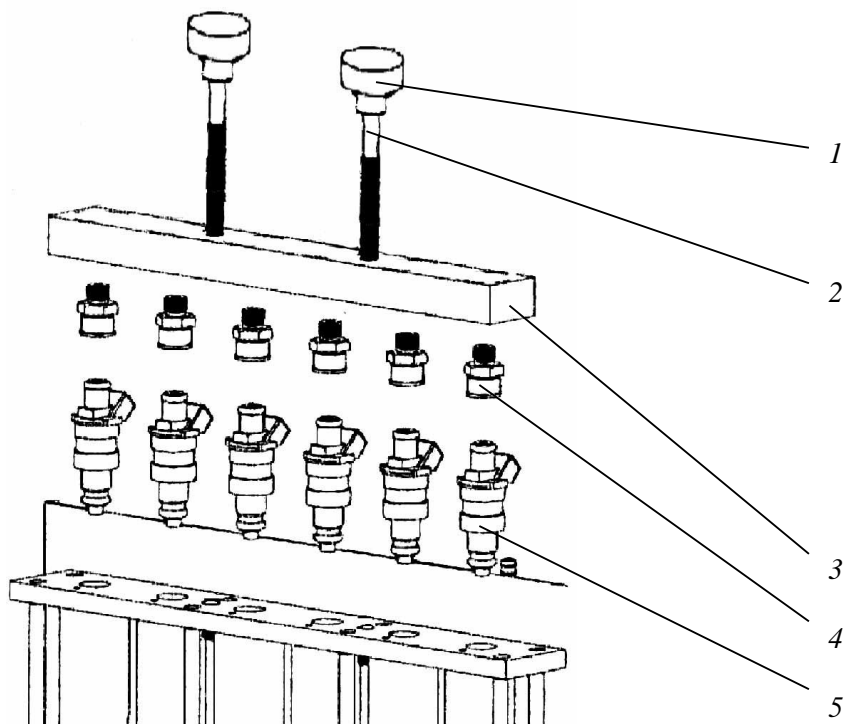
Схема установки форсунок с прямой подачей топлива:
